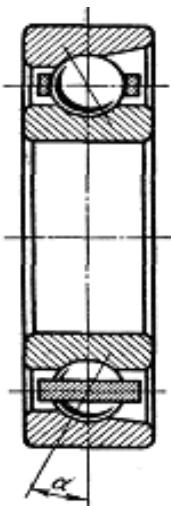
Шариковый радиально-упорный подшипник
